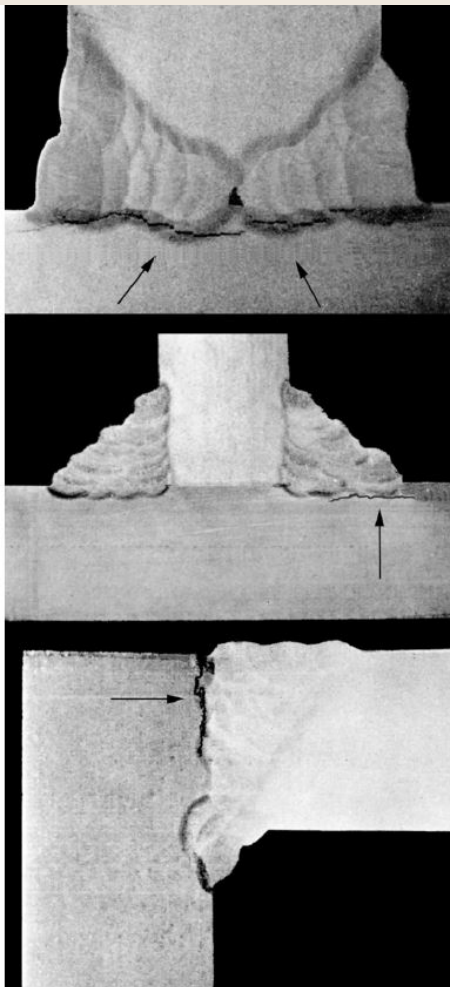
n Fallas por desgarramiento laminar.
